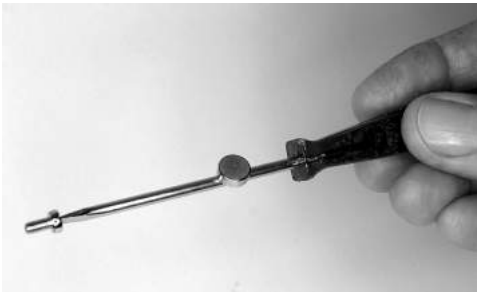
Schraubendreher wird mit Magnet magnetisch und hält die Schraube
